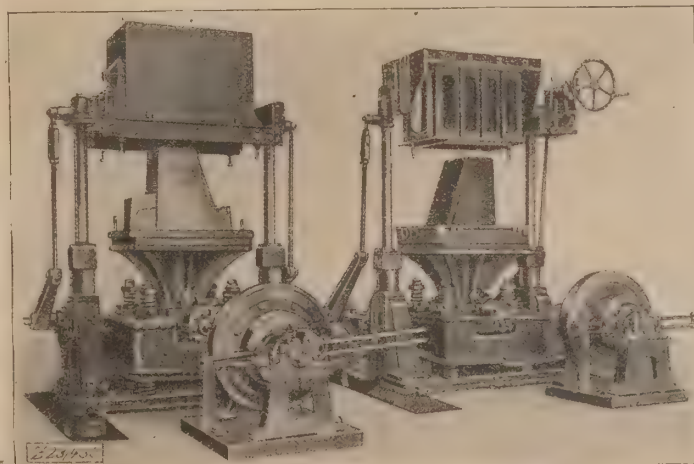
Rüttelformmaschinen für Transmissions- oder Elektromotor-Antrieb.
